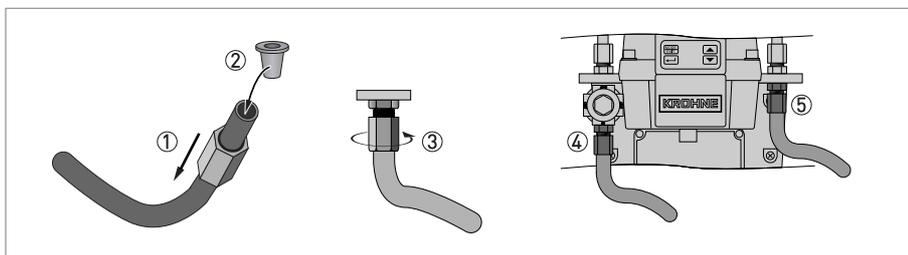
Assemblage des pièces et branchement des tuyaux
